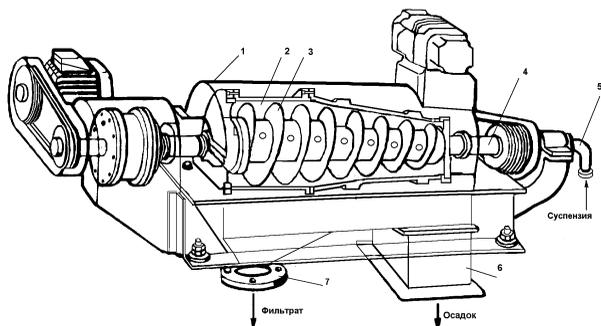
Непрерывно действующая отстойная горизонтальная центрифуга со шнековой выгрузкой осадка: 1-корпус; 2-ротор; 3-шнековое устройство; 4-полюй вал; 5-центральная труба; 6-камера осадка; 7-патрубок для фильтрата
